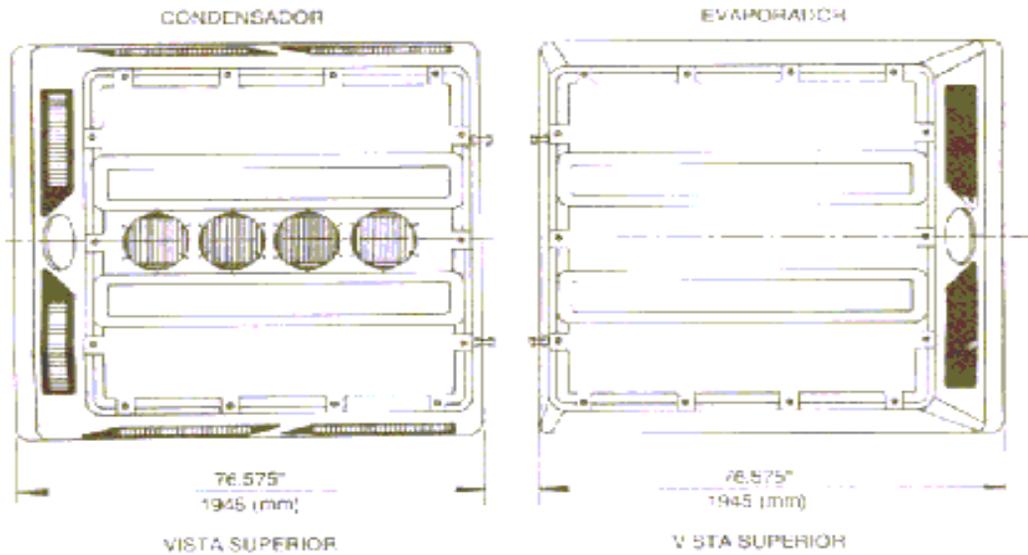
DIMENSIONES DE EQUIPO WIDE UNIT⁴⁵
